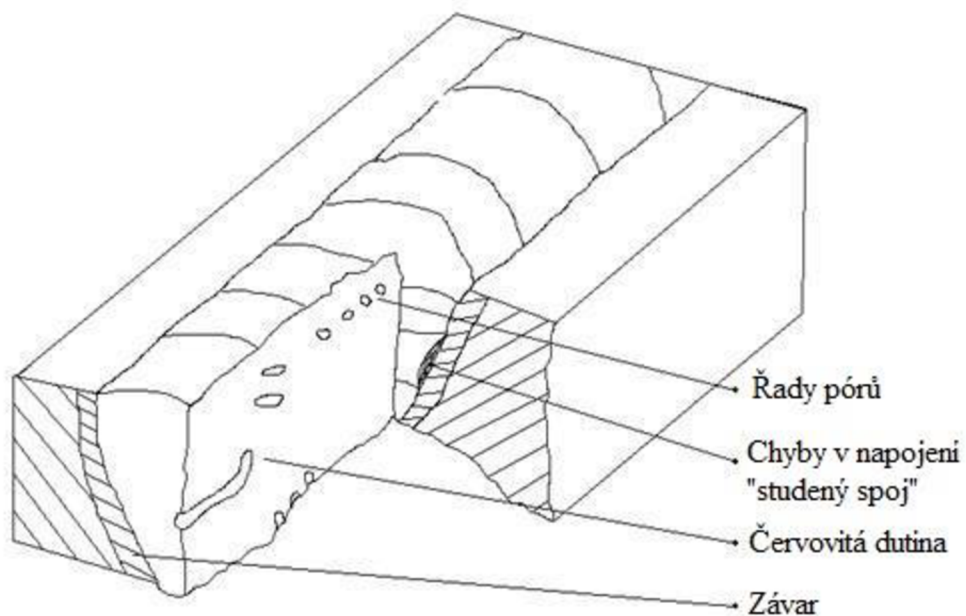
Vady ve svarech dle tvaru a polohy [38].
